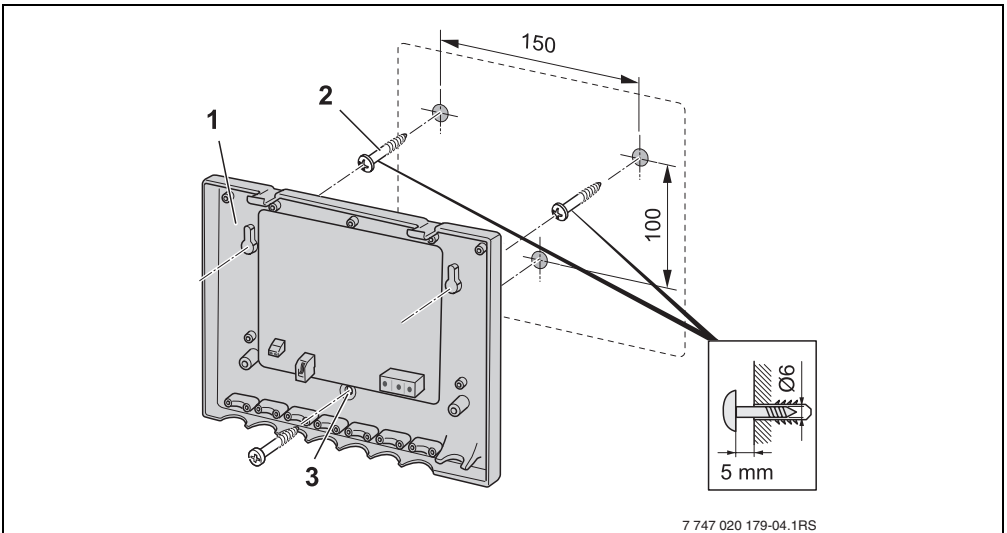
Sockel des Easycom Switch an einer Wand montieren
